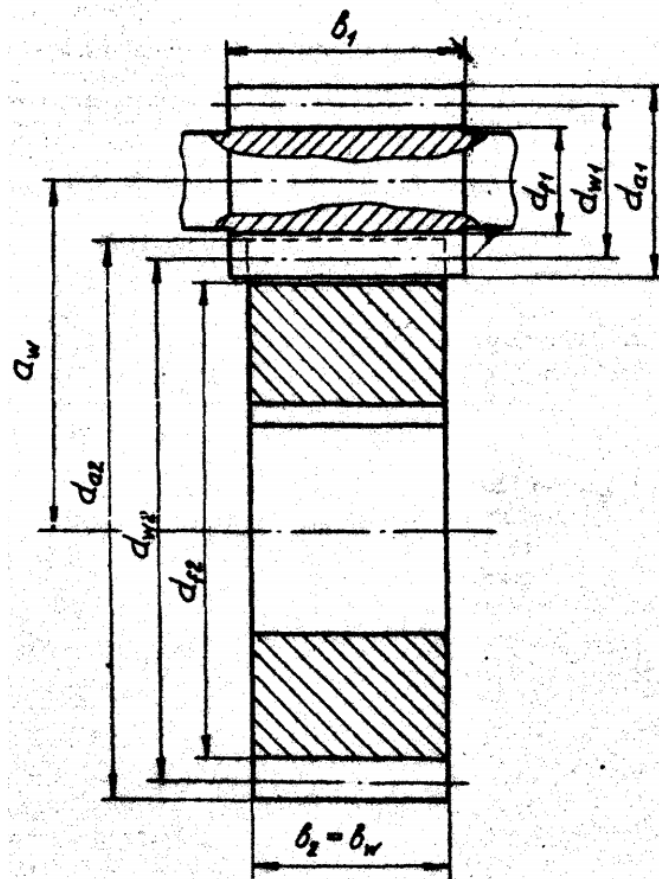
Геометрические параметры цилиндрической зубчатой передачи
